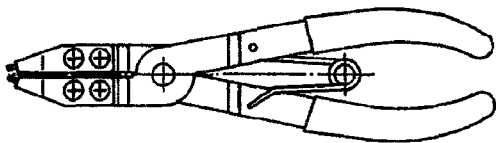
Спецпассатижи для снятия и установки внутренних упорных колец
